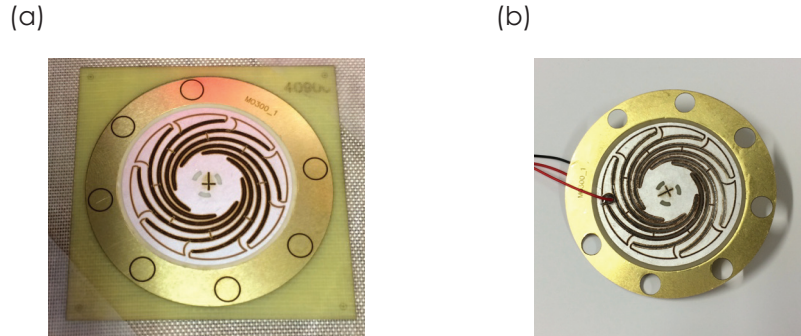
SPIRALE RÉALISÉE PAR MICRO USINAGE LASER
